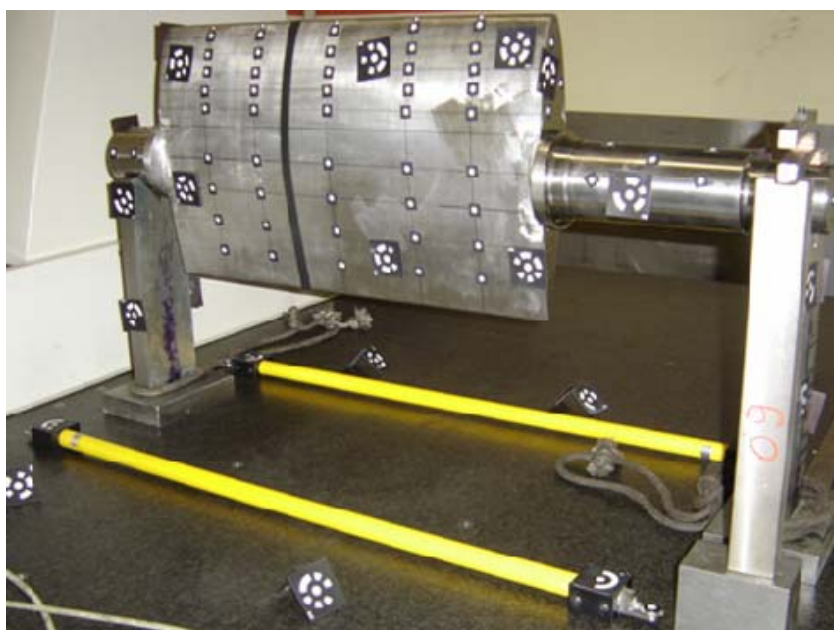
Palheta diretriz montada sobre a MMC, pronta para ser medida com o sistema TRITOP, junto aos padrões de comprimento.
